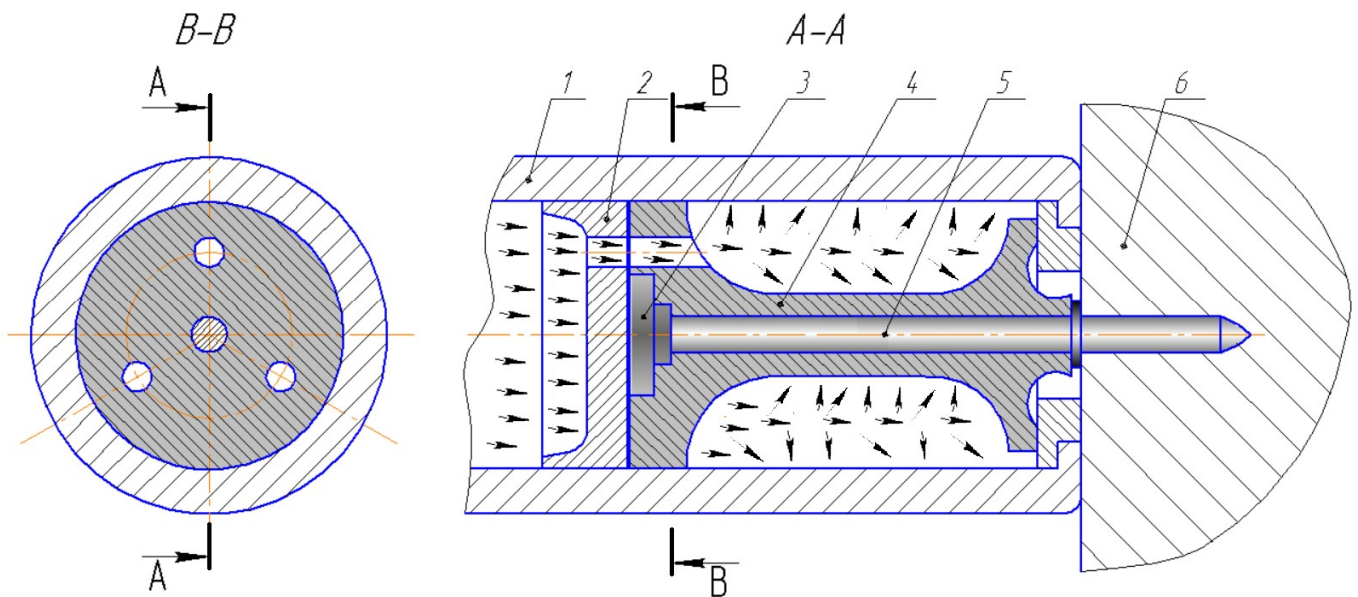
Разработанная конструкция ствольной насадки к строительному монтажному пистолету
